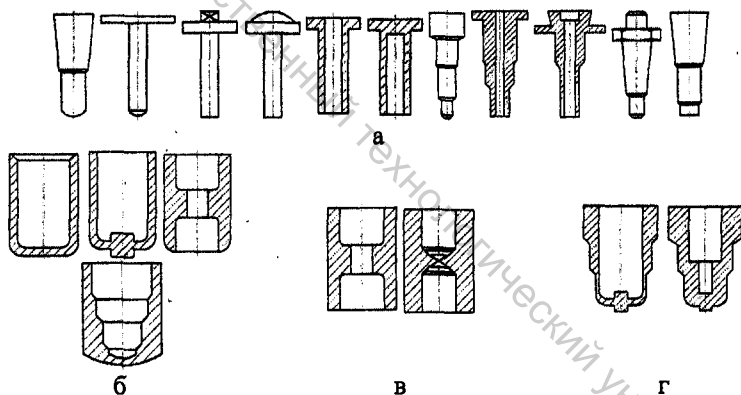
Заготовки типа стержней и стаканов, получаемые холодной объемной штамповкой:
